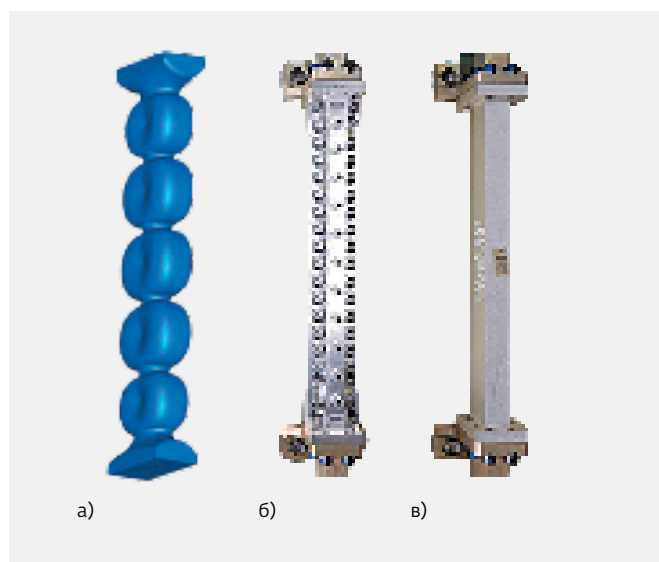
Полосовой фильтр, полоса пропускания 14,00–14,25 ГГц: а – 3D-модель внутренней полости (канала) фильтра, б – фильтр, изготовленный путем фрезерования, в – напечатанный фильтр. Источник: Airbus Defense and Space
